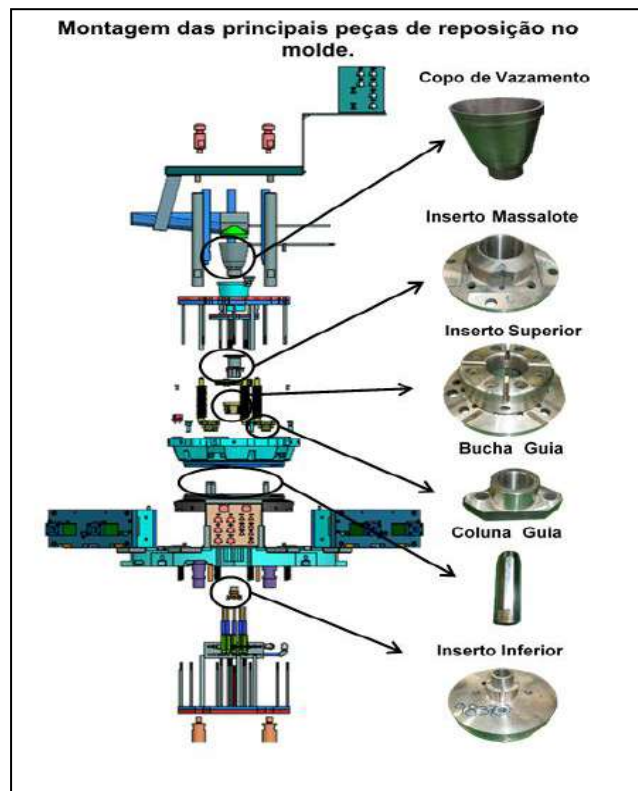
Desenho do molde da roda, destacando as principais peças de reposição.
